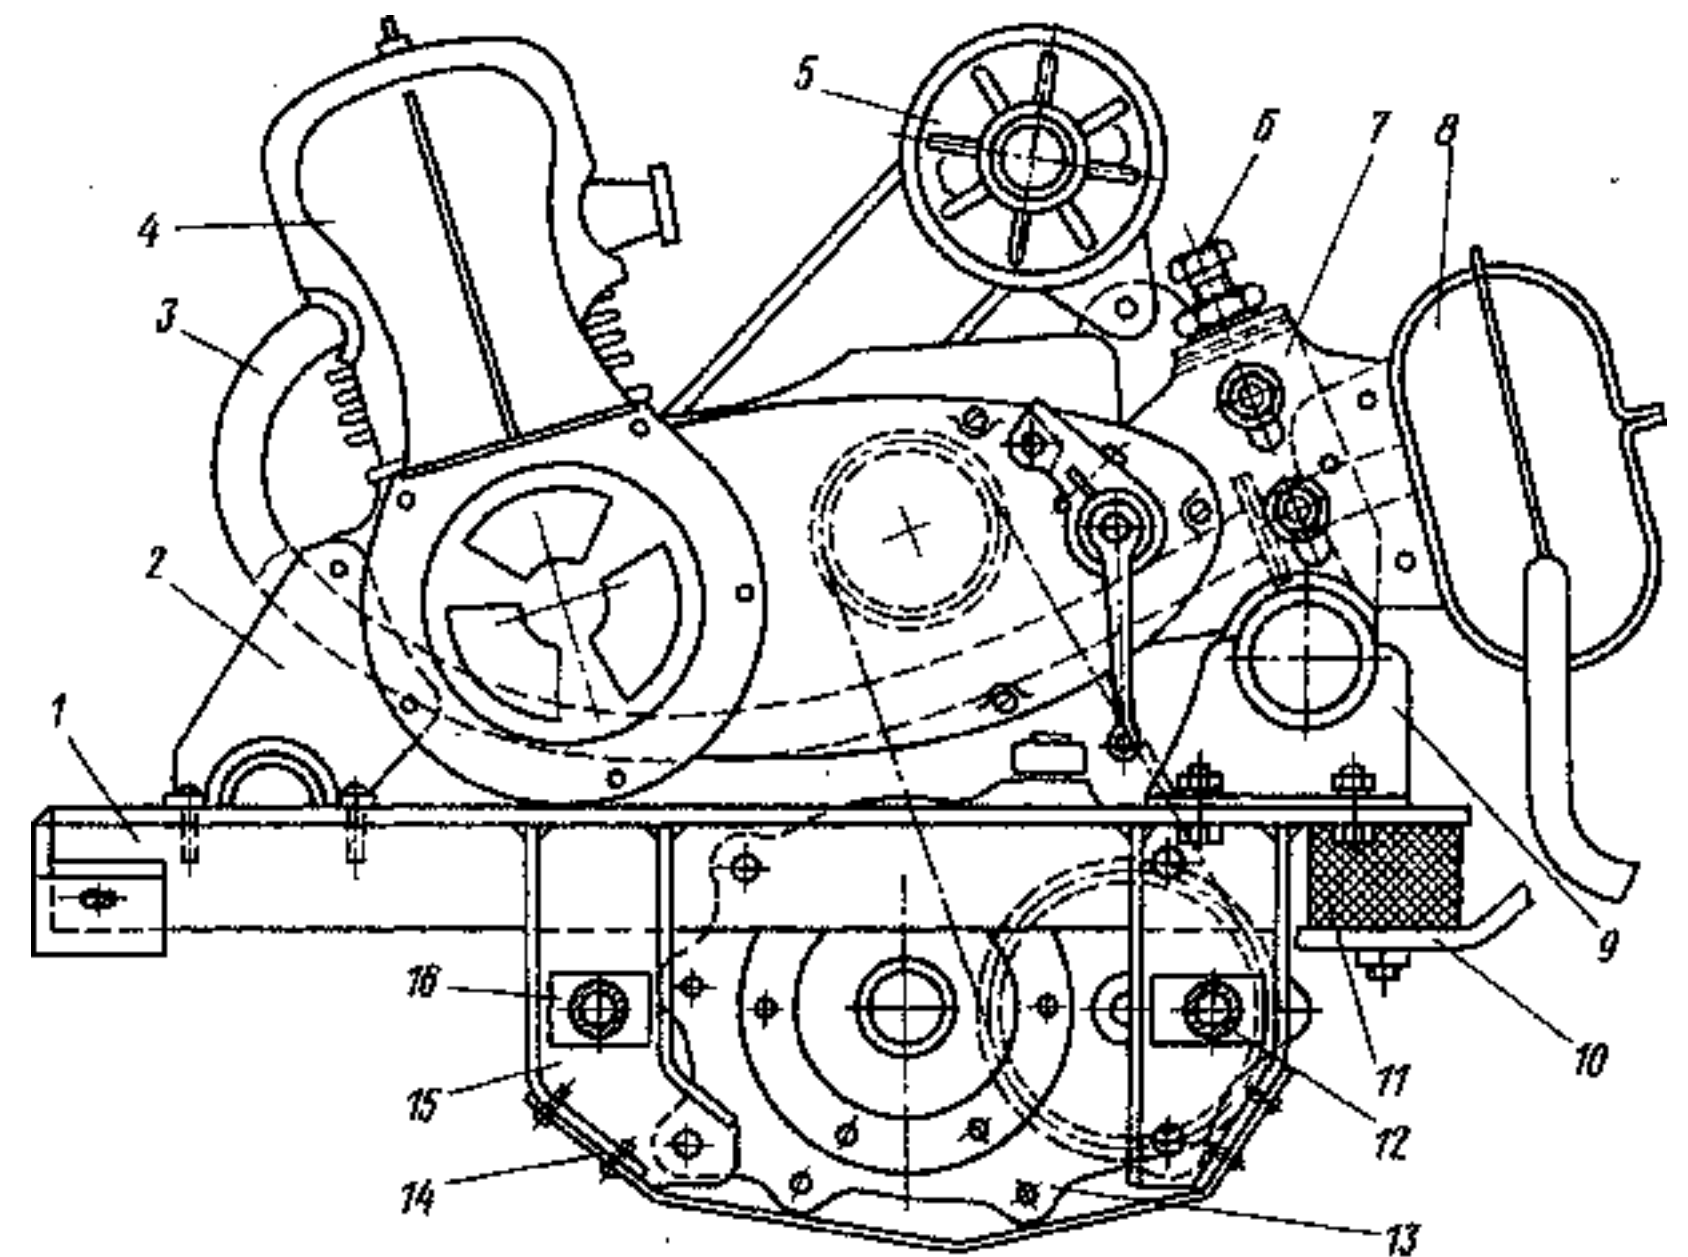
Схема установки двигателя и главной передачи на подрамнике:
